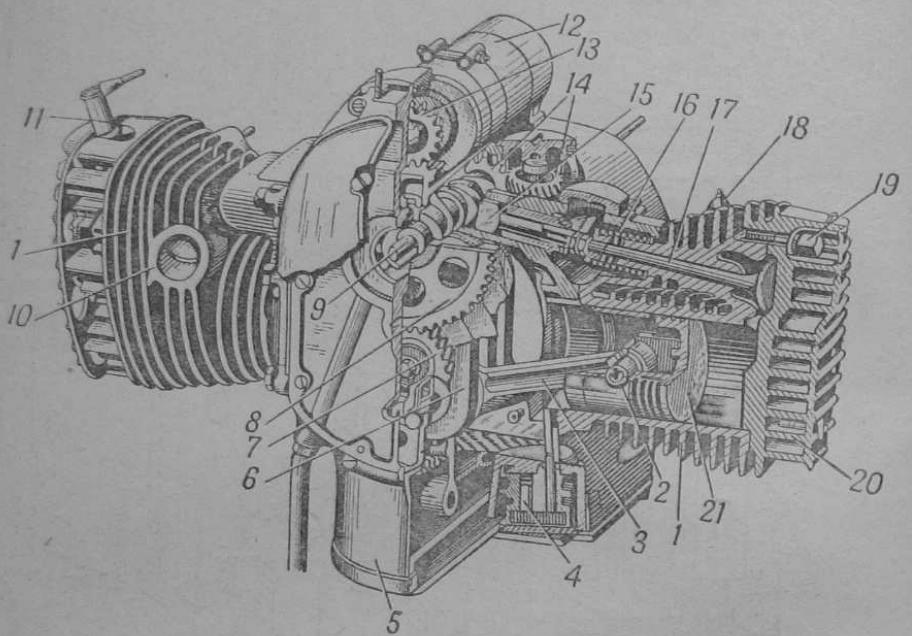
Двигатель мотоцикла М-72. Наружный вид с вырезом:
